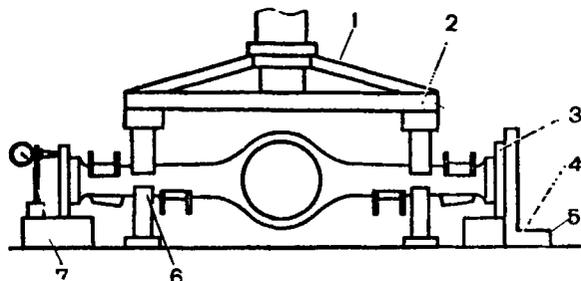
Схема правки балки заднего моста: 1 - гидроцилиндр; 2 - прижимная траверса; 3 - фланец А.70172; 4 - угольник; 5 - стол пресса; 6 - упор; 7 - стойка индикатора
